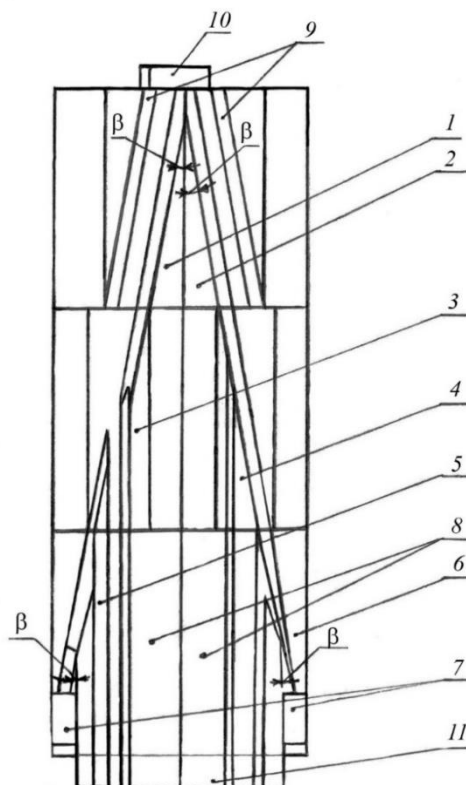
Схема инструмента ПКП для детали «Вал»
